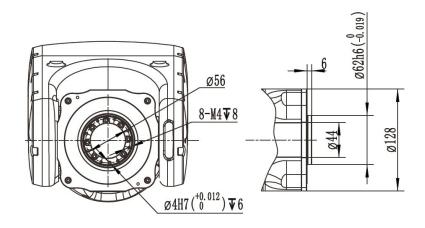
Размеры фланца CRP-RH18-20 (W).
